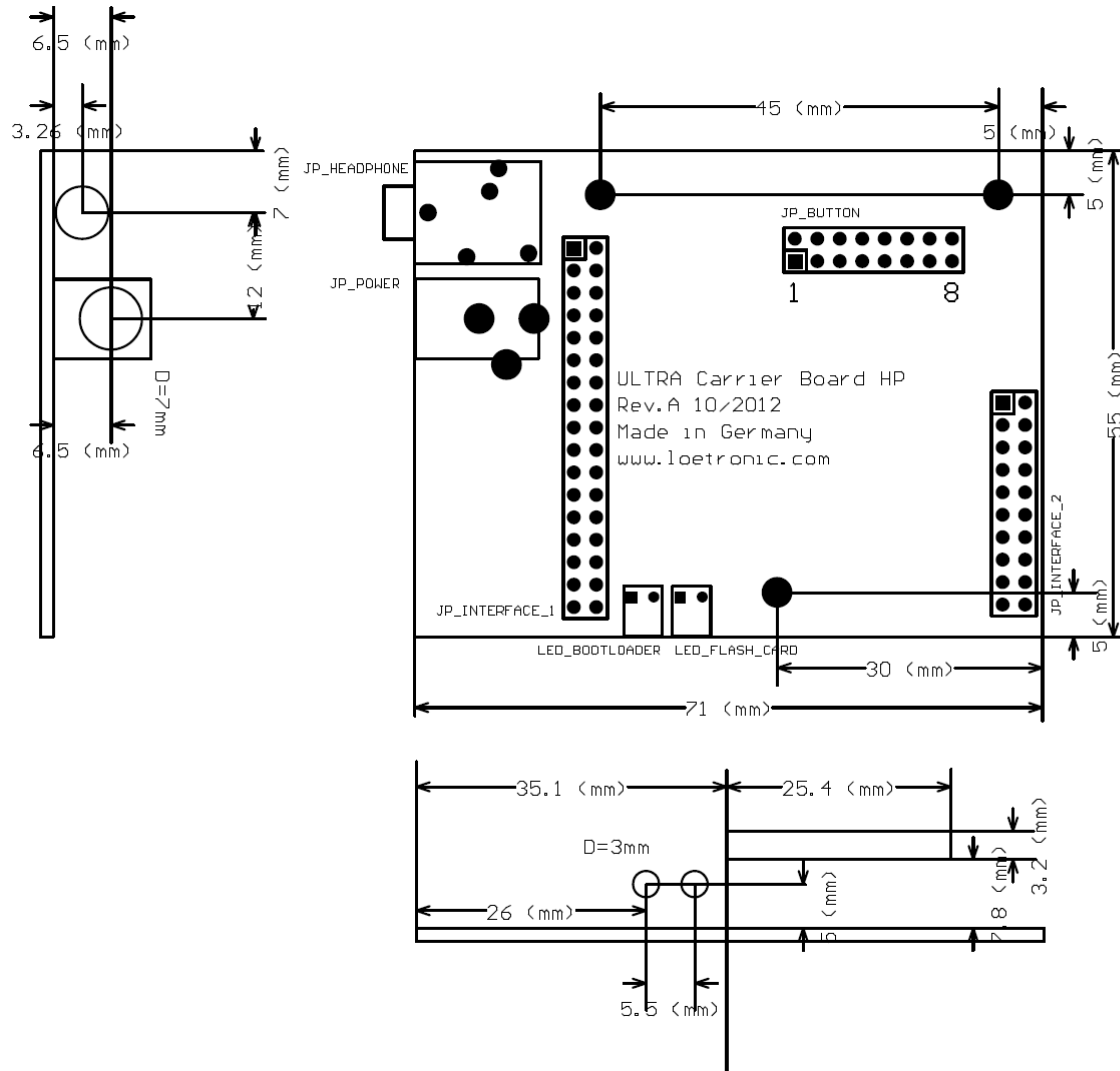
Fallguy ULTRA Carrier Board HP Rev.A - Abmessungen
